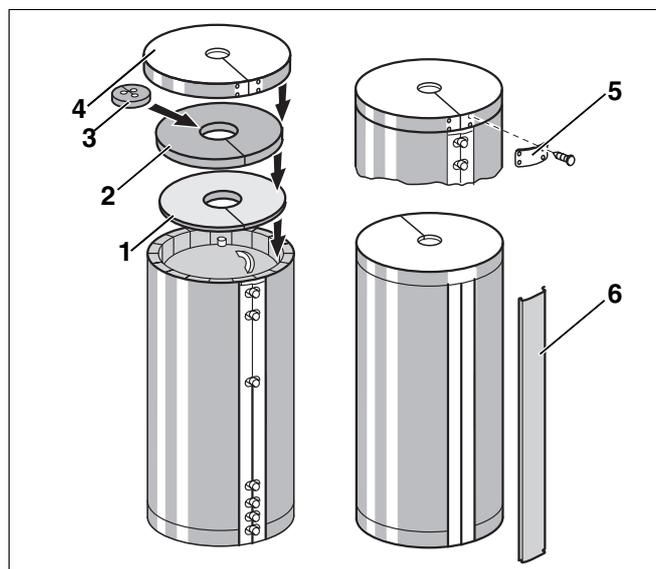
Montage Wärmeschutz (Prinzipdarstellung)
